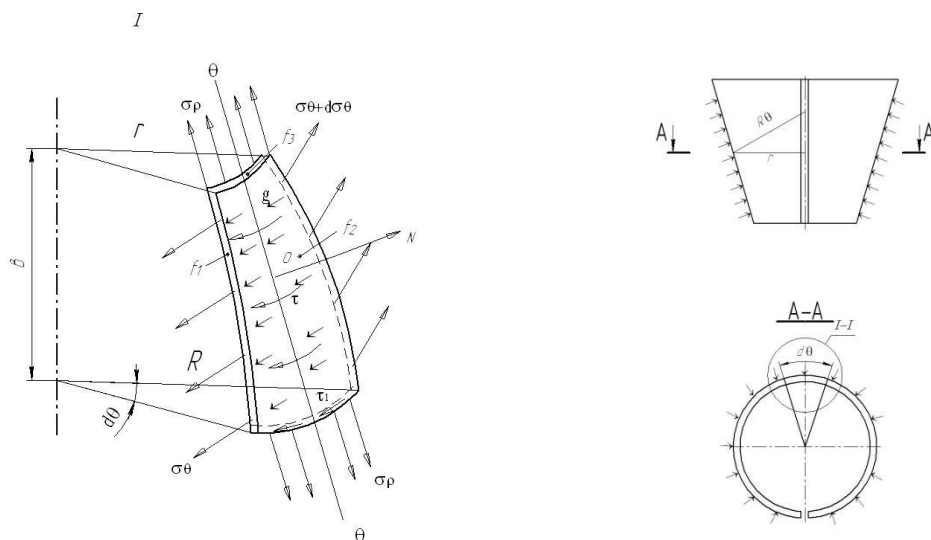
Схема к определению процесса формовки заготовки, согнутой в конус, без соединения вдоль образующей
